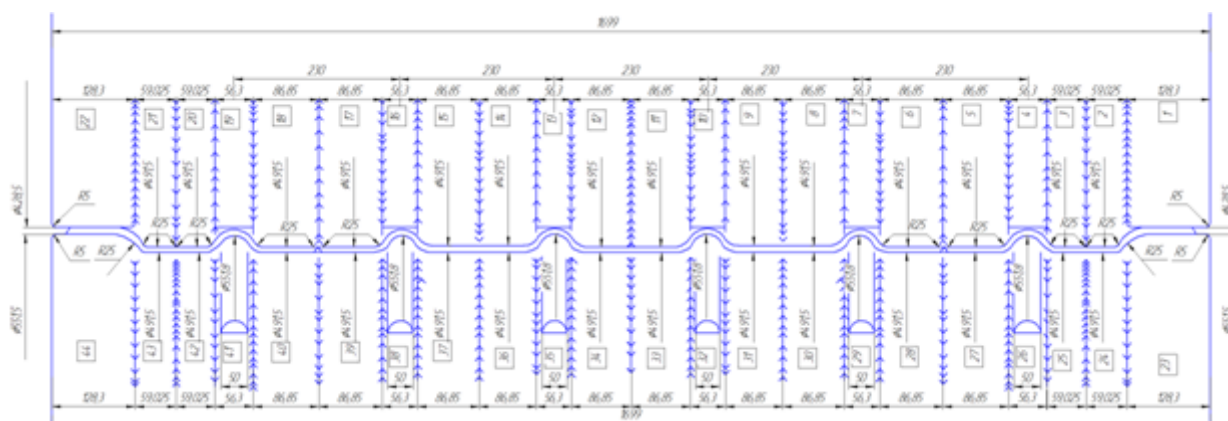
Калибровка валков для производства профиля крышки люка, компенсирующая износ формующих элементов
